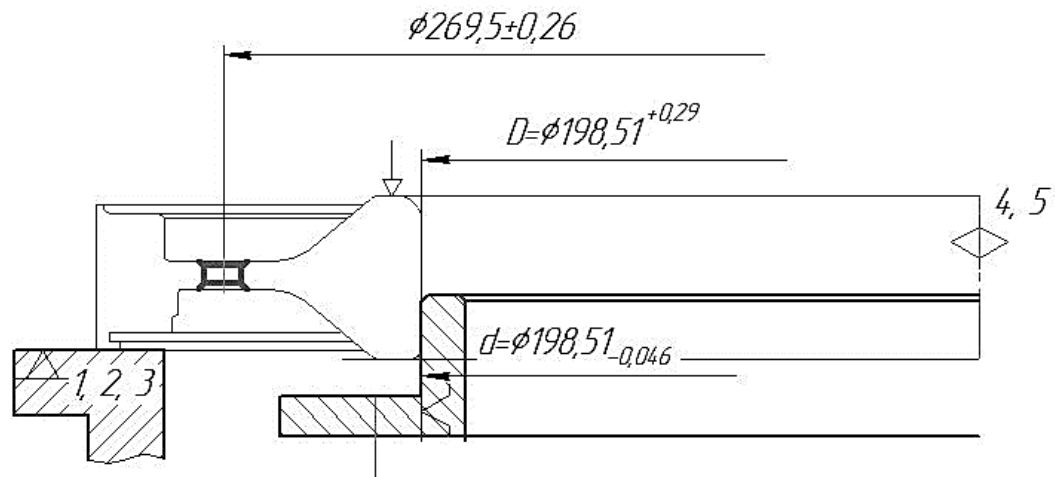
Схема встановлення деталі жорсткий циліндричний палець.
